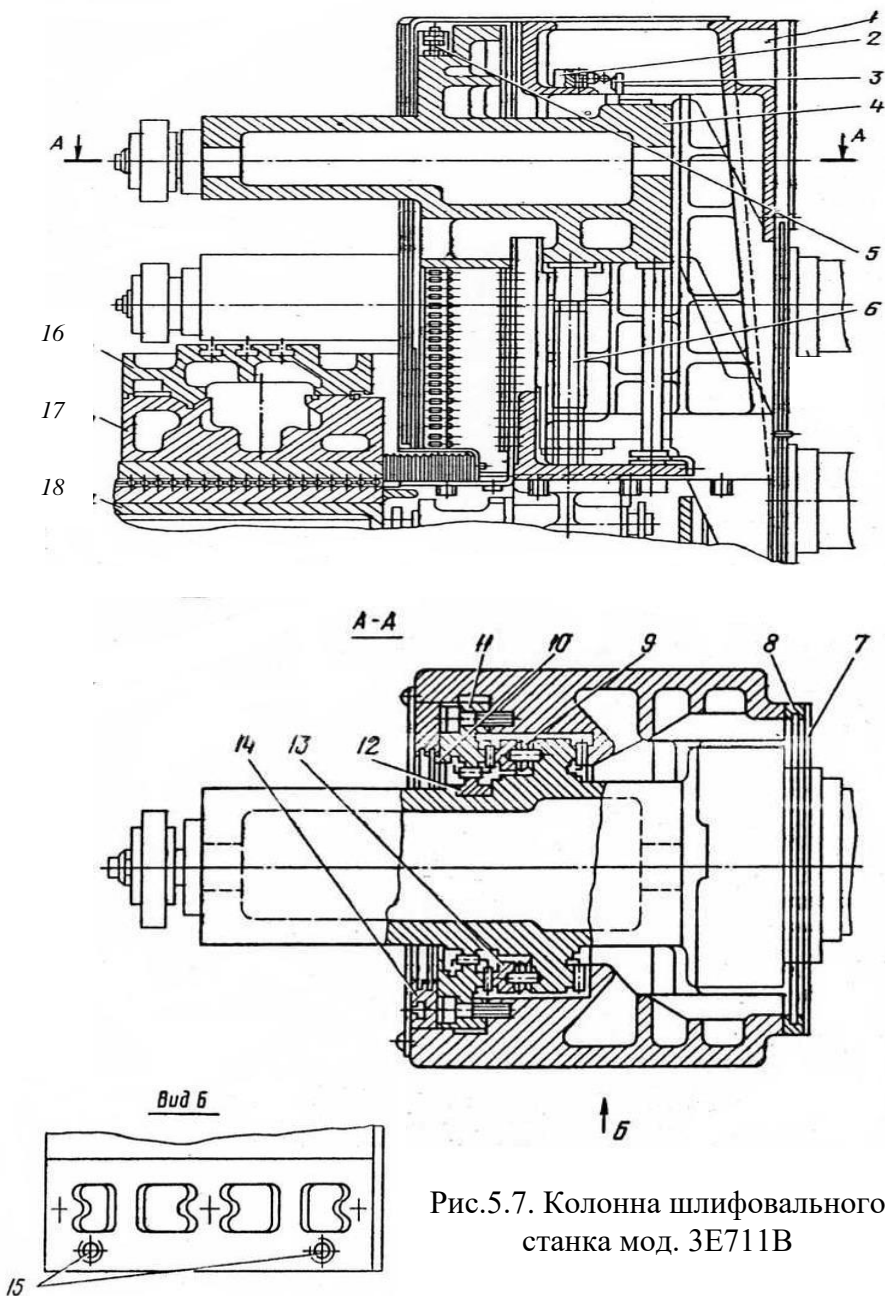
Колонна шлифовального станка мод. 3E711B
